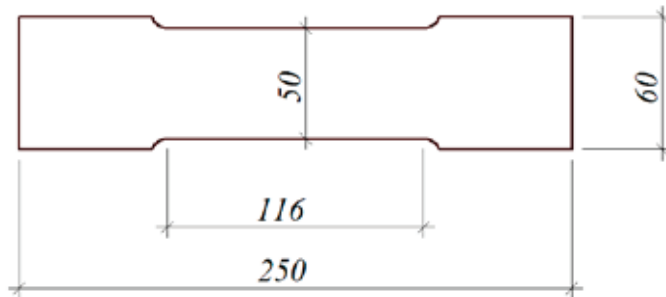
Стандартный образец-лопатка для испытания на разрыв
